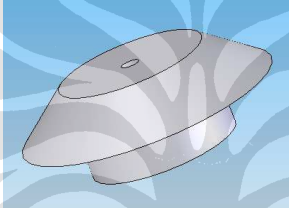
assembly komponen pompa toothpaste dispenser
